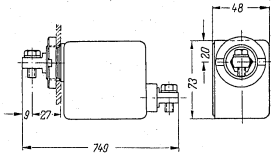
für zentrale Schraubbefestigung (Bauform b)
